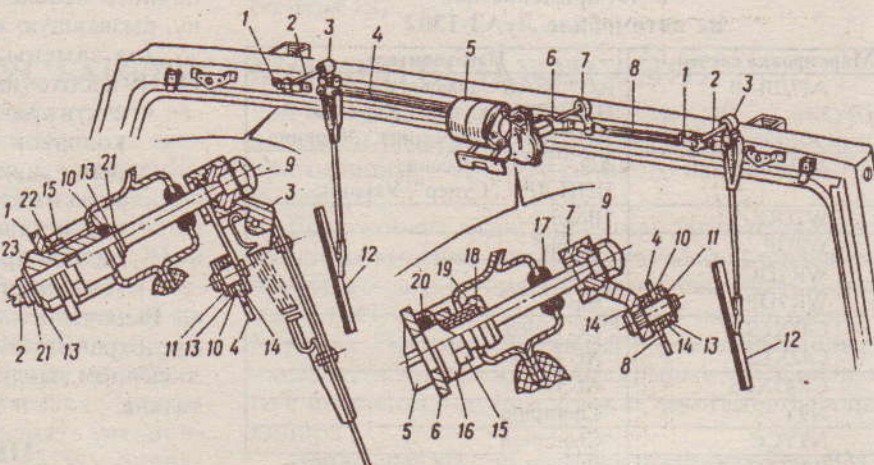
Стеклоочиститель: 1 - боковой кронштейн; 2 - ось рычага; 3 - рычаг с головкой в сборе; 4 - левая тяга; 5 - редуктор стеклоочистителя с электродвигателем в сборе; 6 - центральный кронштейн; 7 - поводок; 8 - правая тяга; 9 - гайка крепления рычага; 10 - уплотнительная шайба; 11 - пружинный шплинт; 12 - щетка в сборе; 13 - шайба; 14 - дистанционная шайба; 15 - гайка; 16 - шайба; 17 - уплотнительная втулка; 18 - манжета; 19 - гайка манжеты; 20 - прокладка; 21 - пружинное кольцо; 22 - шайба; 23 - втулка
